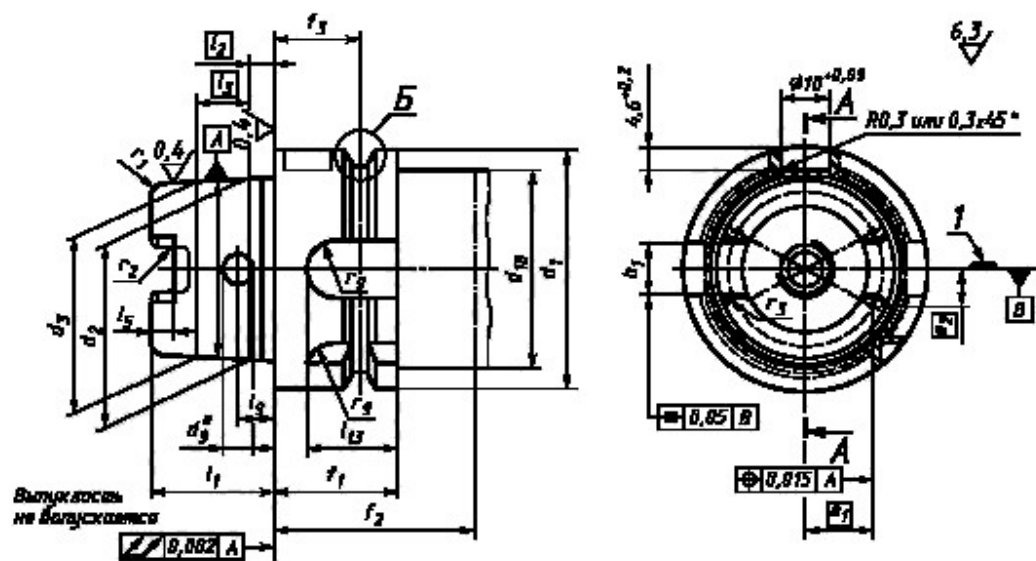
Хвостовики інструментів порожнисті конічні типу HSK
